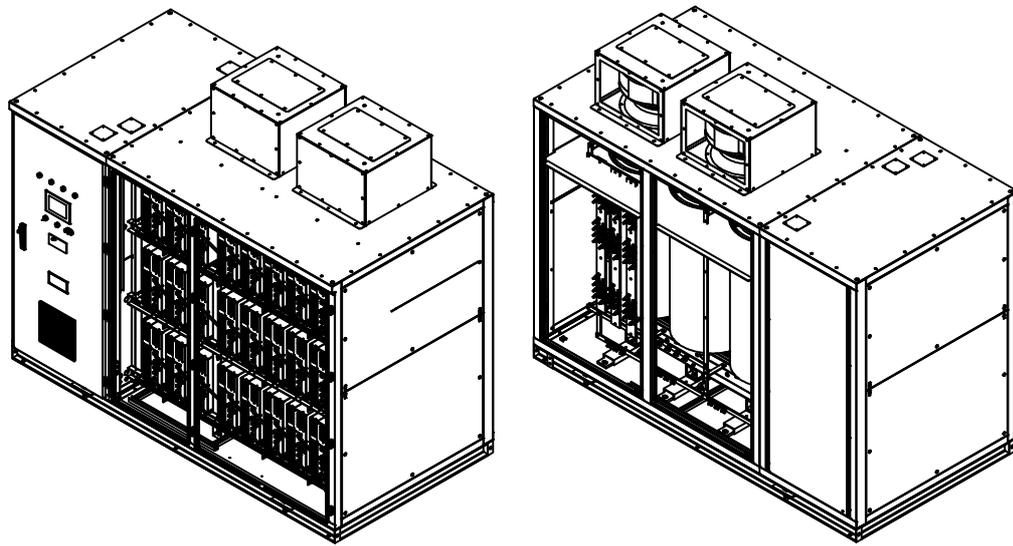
Внешний вид ПЧ (конструкция G3).
